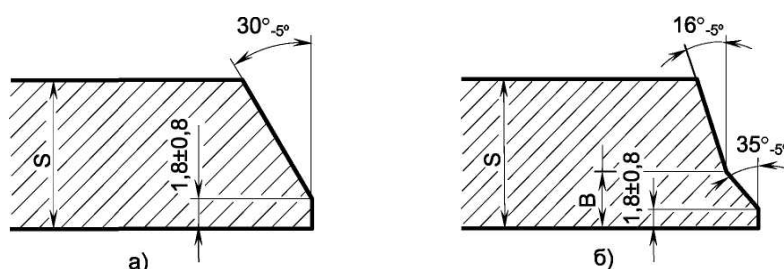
Форма разделки кромок труб для комбинированной сварки с применением Комплекса автоматической сварки
